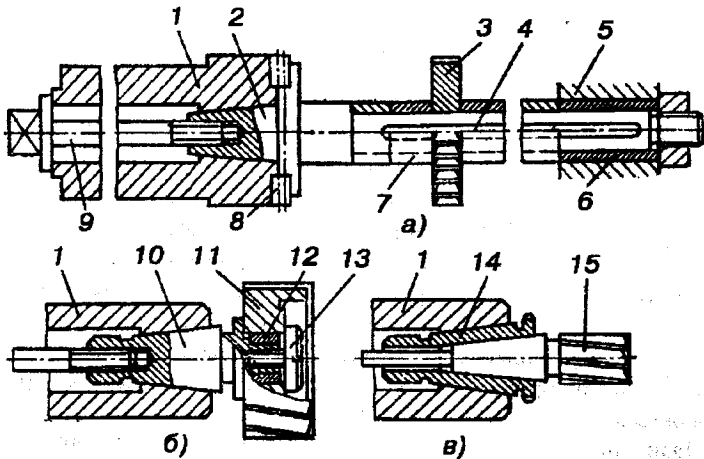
Схеми установки і закріплення фрез на верстатах
